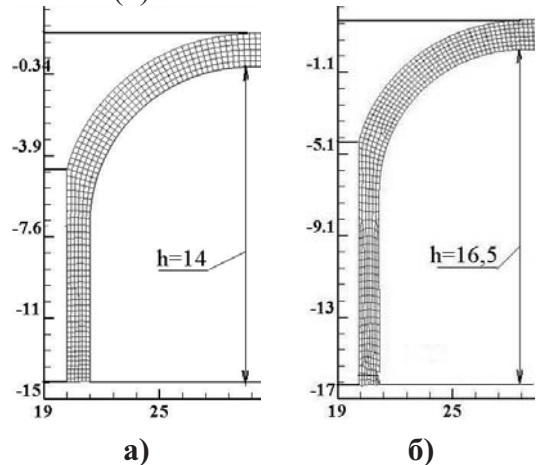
Размеры (в миллиметрах) заготовок после отбортовки и утонения: а- традиционная заготовка, б- спрофилированная заготовка
